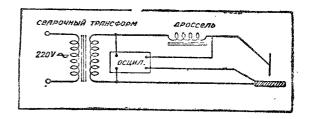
Принципиальная схема установки для дуговой сварки переменным током
